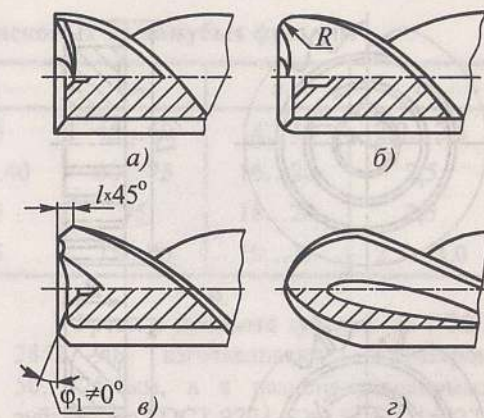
Формы торцевой части концевых быстрорежущих фрез:
